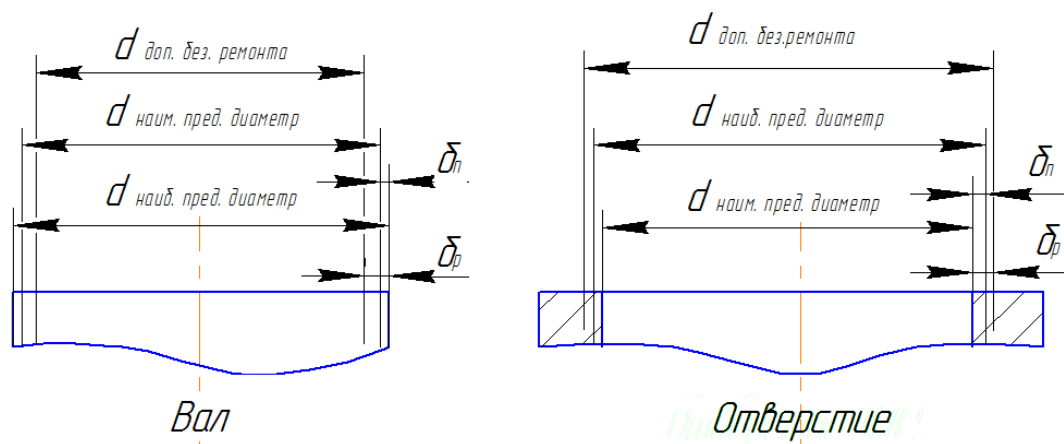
Ремонтные и производственные допуски рабочих поверхностей деталей
